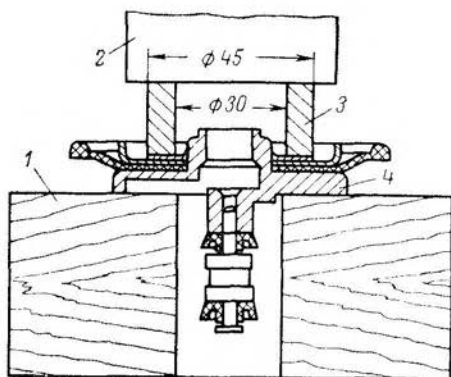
Напрессовка пластинчатой шайбы на клапан управления:
